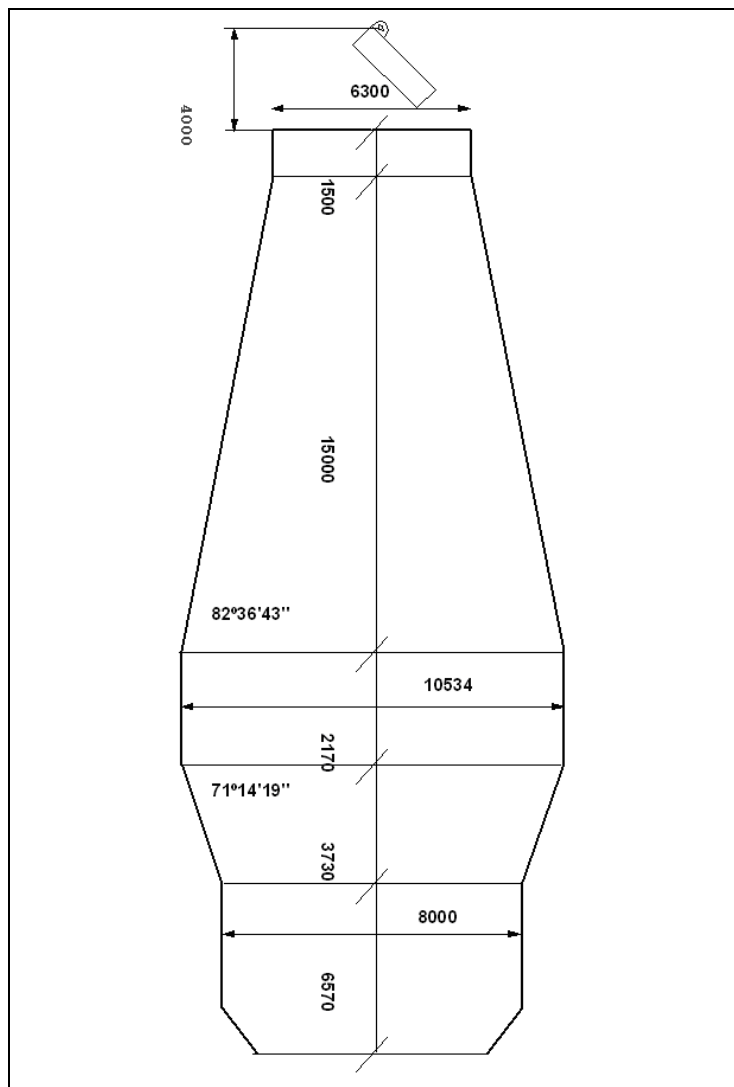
Dimensões Estruturais do Alto-Forno 02 da ArcelorMittal Tubarão
